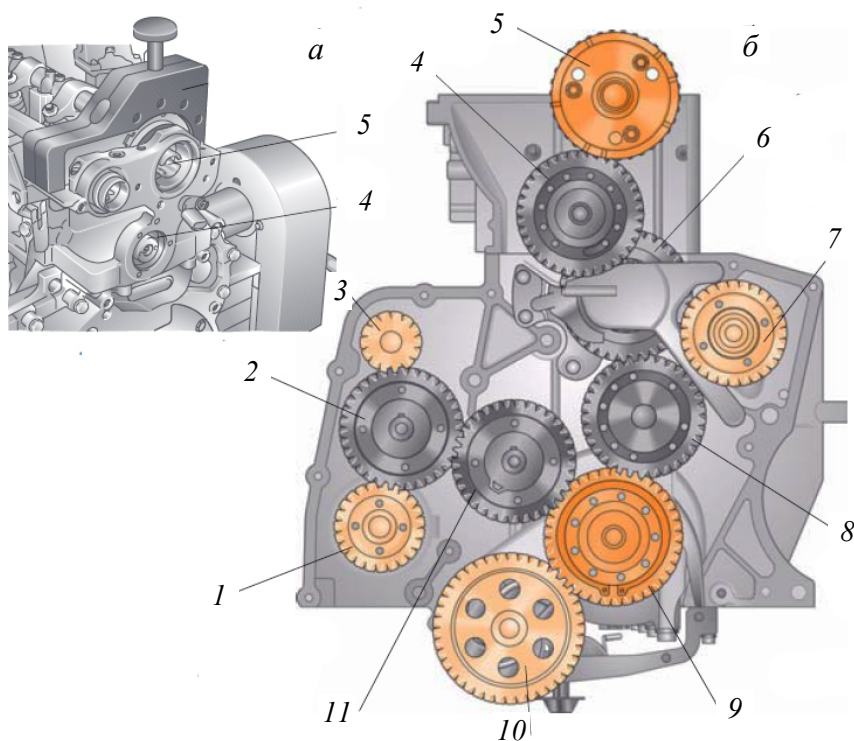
Шестеренчатый привод распределительного вала и вспомогательных агрегатов:
